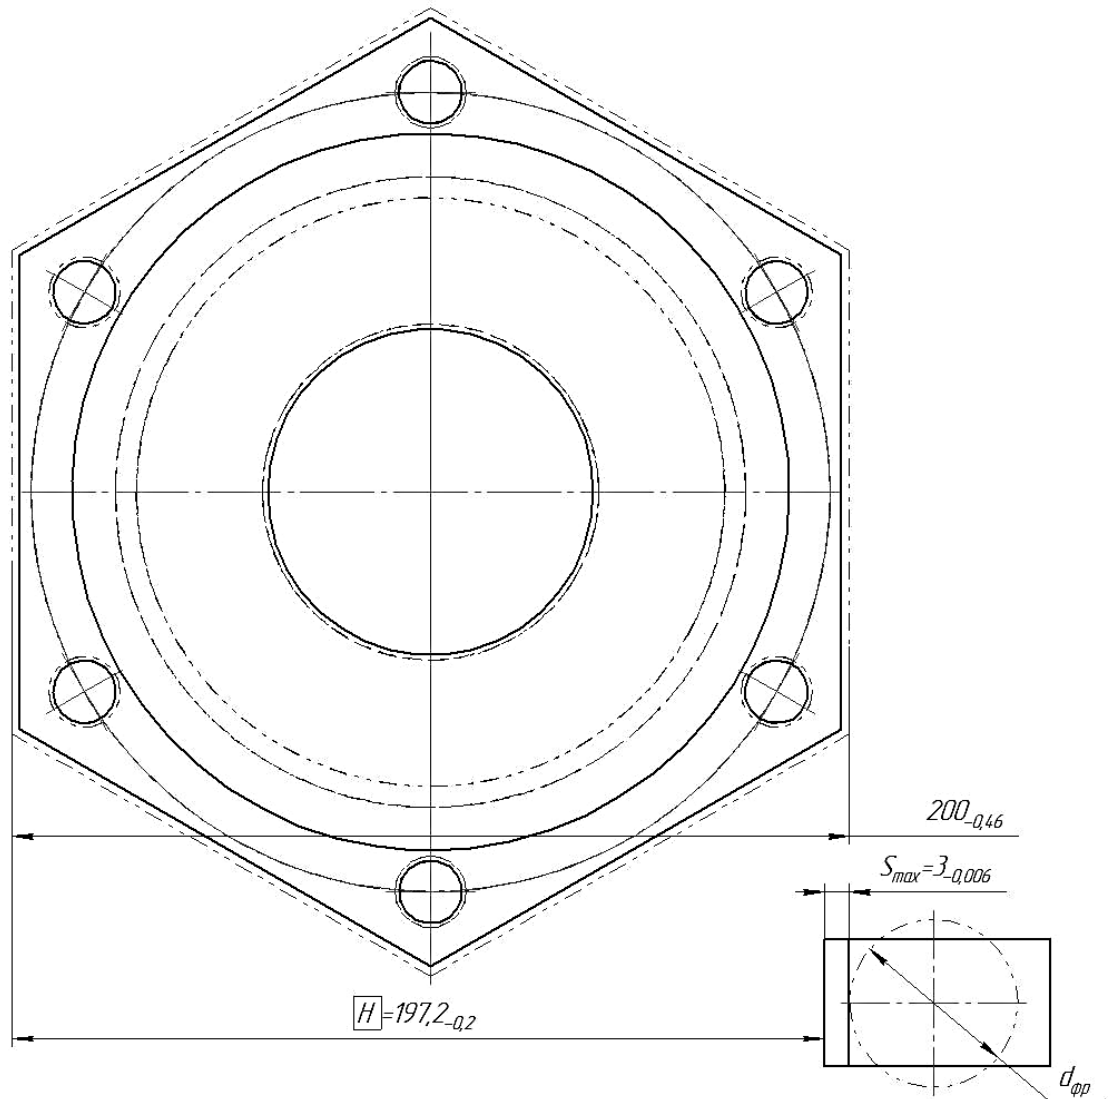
Схема налаштування інструмента для фрезерування
